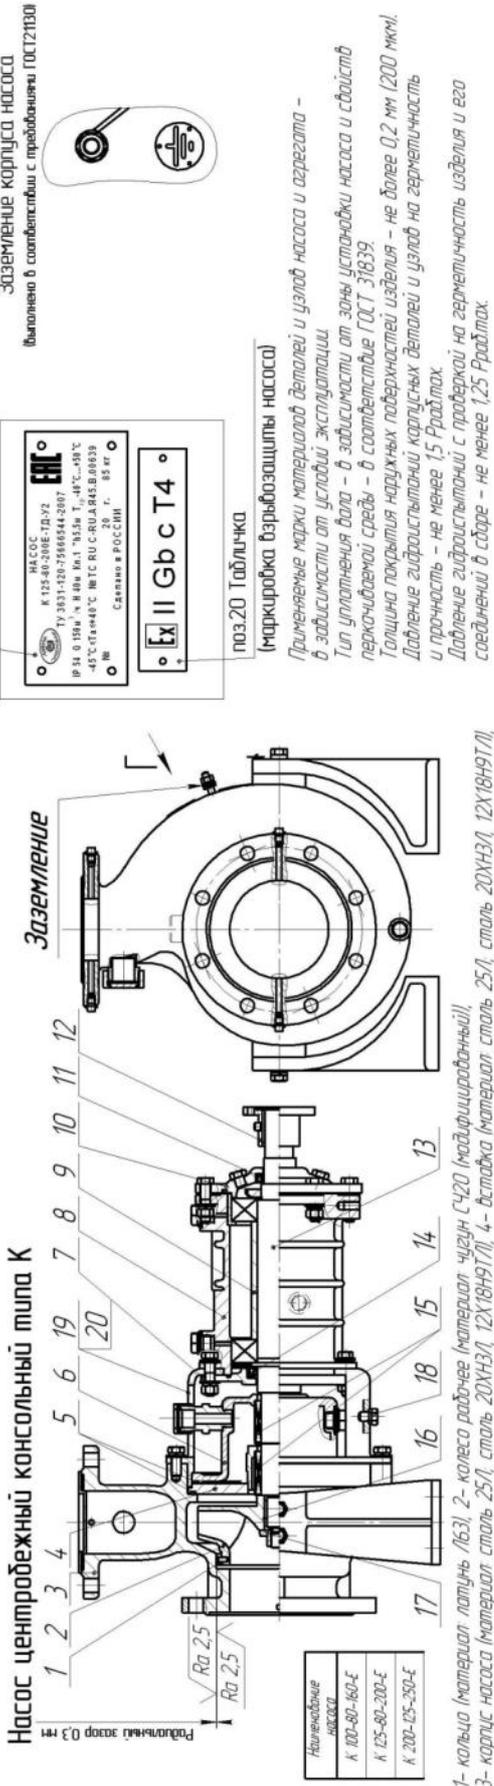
Чертеж средств взрывозащиты. Насосы центробежные консольные типа К (с фланцевым присоединением корпуса) и агрегаты электронасосные на их базе
